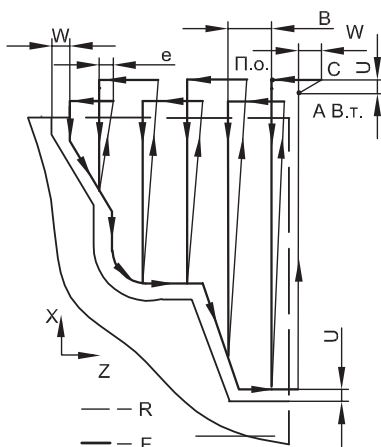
Багатопохідний чорновий поперечний цикл G62
